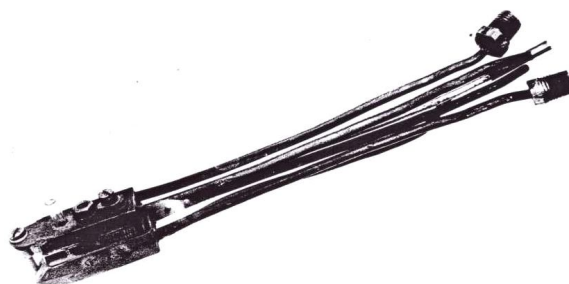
Малогабаритная плазменная горелка для наплавки шеек коленчатого вала
